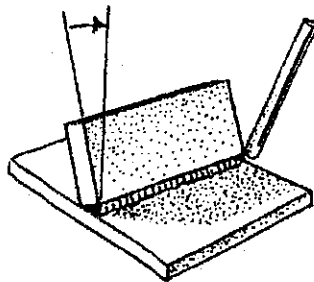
Técnica de retroceso en la aplicación de la soldadura.
